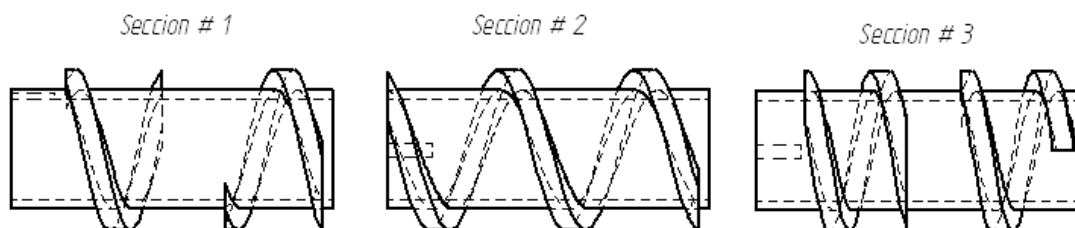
, Secciones del tornillo extrusor, Fuente, López William.
